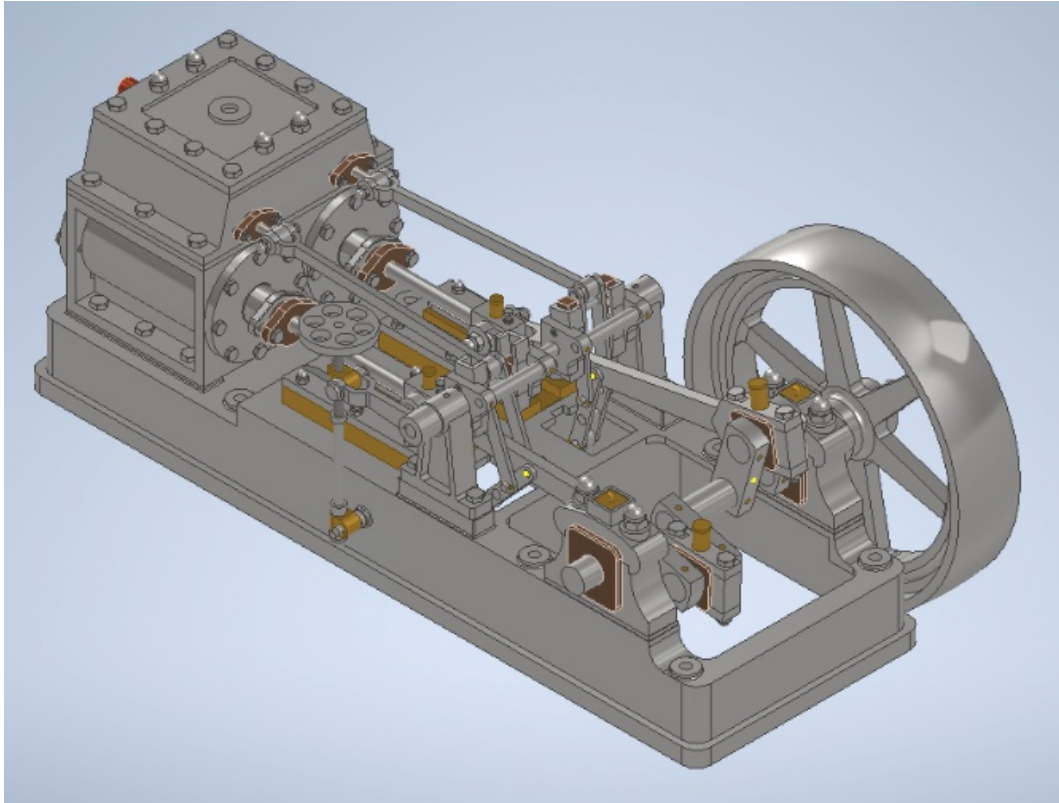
Perspectiva axonométrica del ensamblaje final del conjunto (vista frontal).
